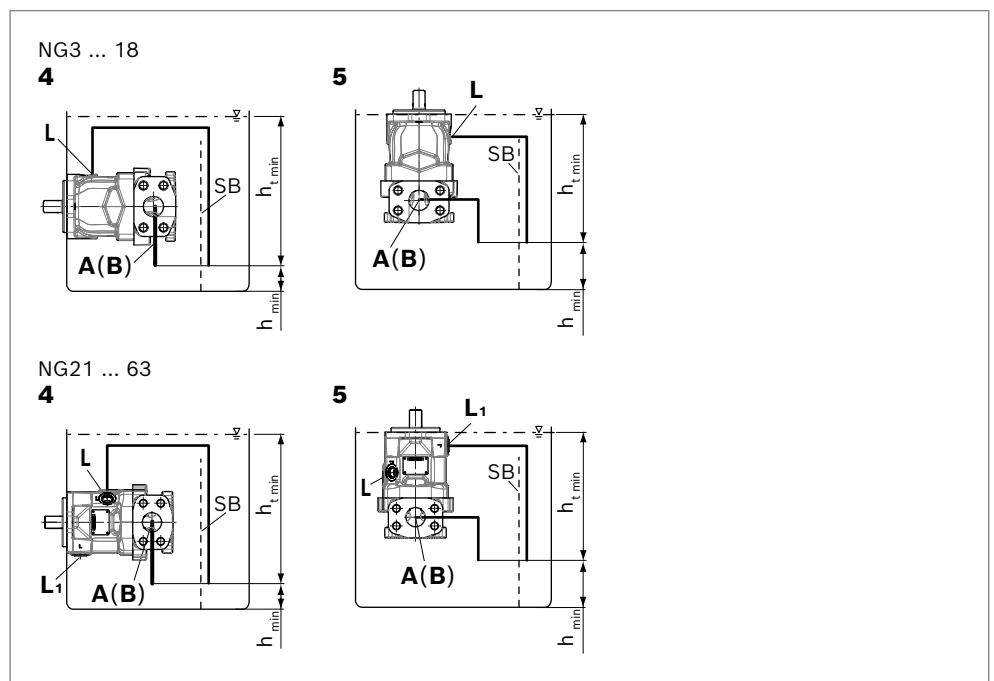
Tankeinbau A10FZO mit Einbaulage 4–5
